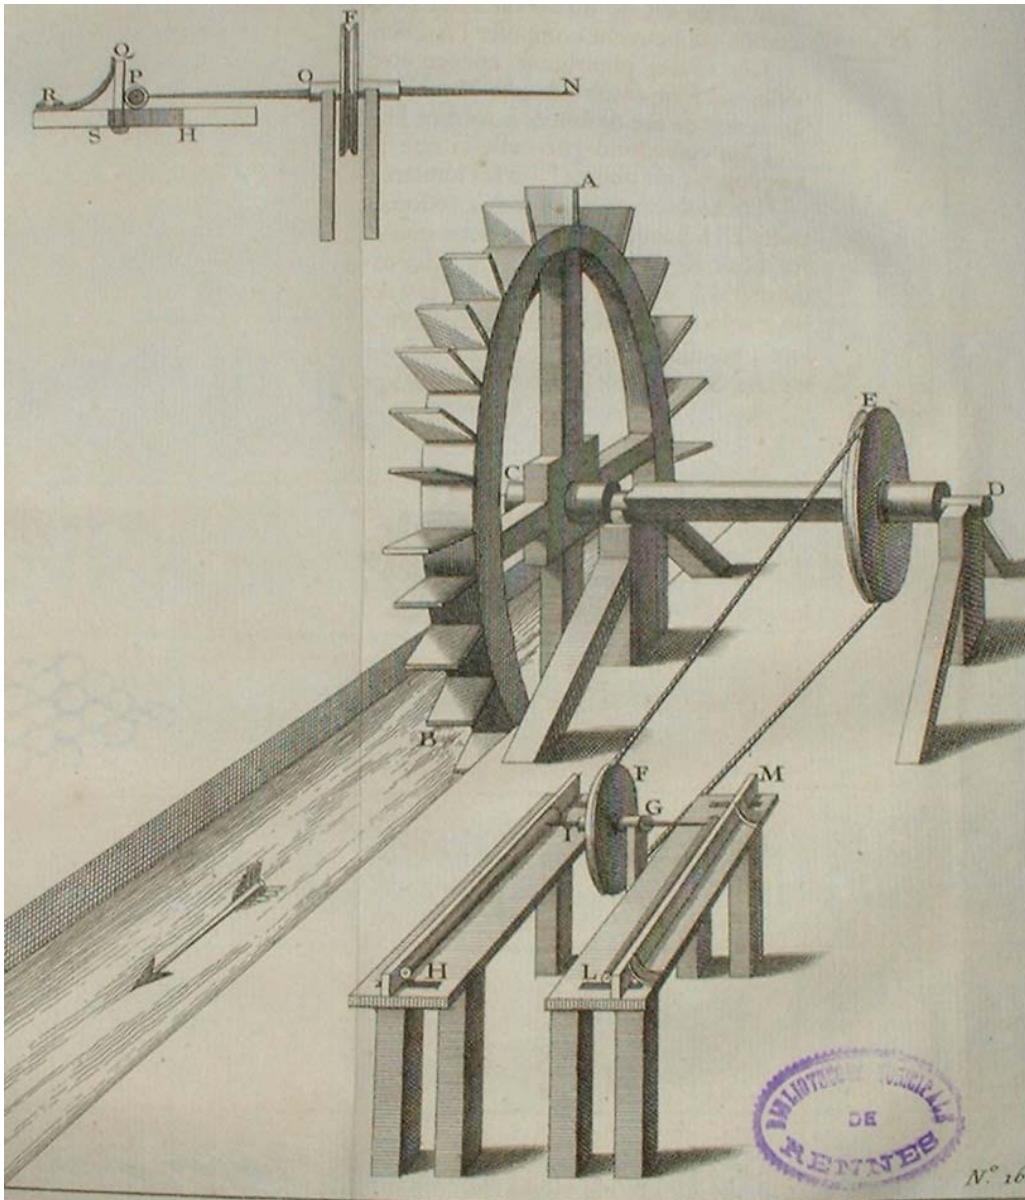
, machine à percer, machines et inventions, Gallon, 16 x 21 cm.
